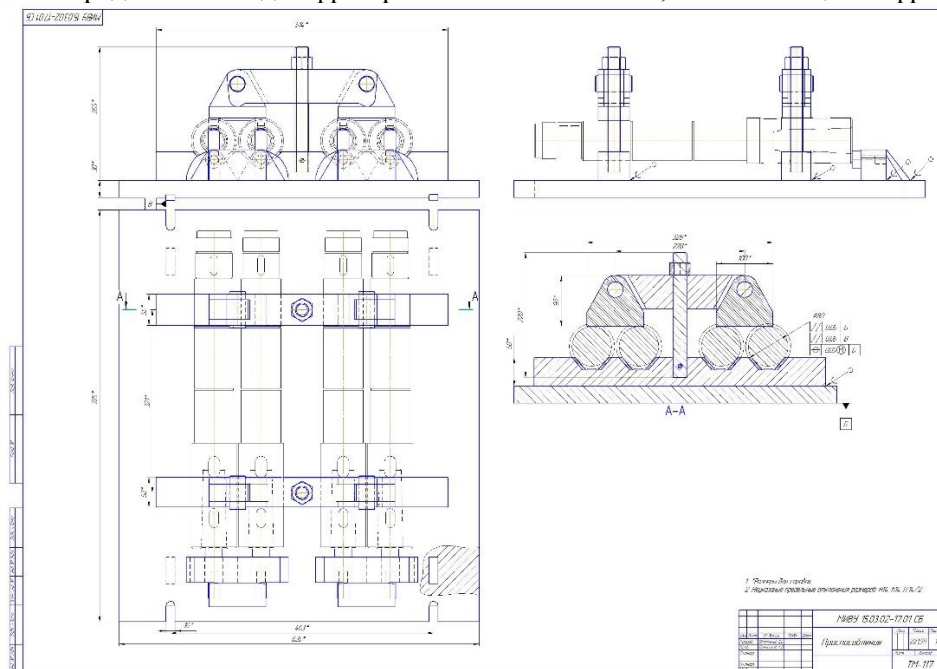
Общий вид многоместного фрезерного приспособления
